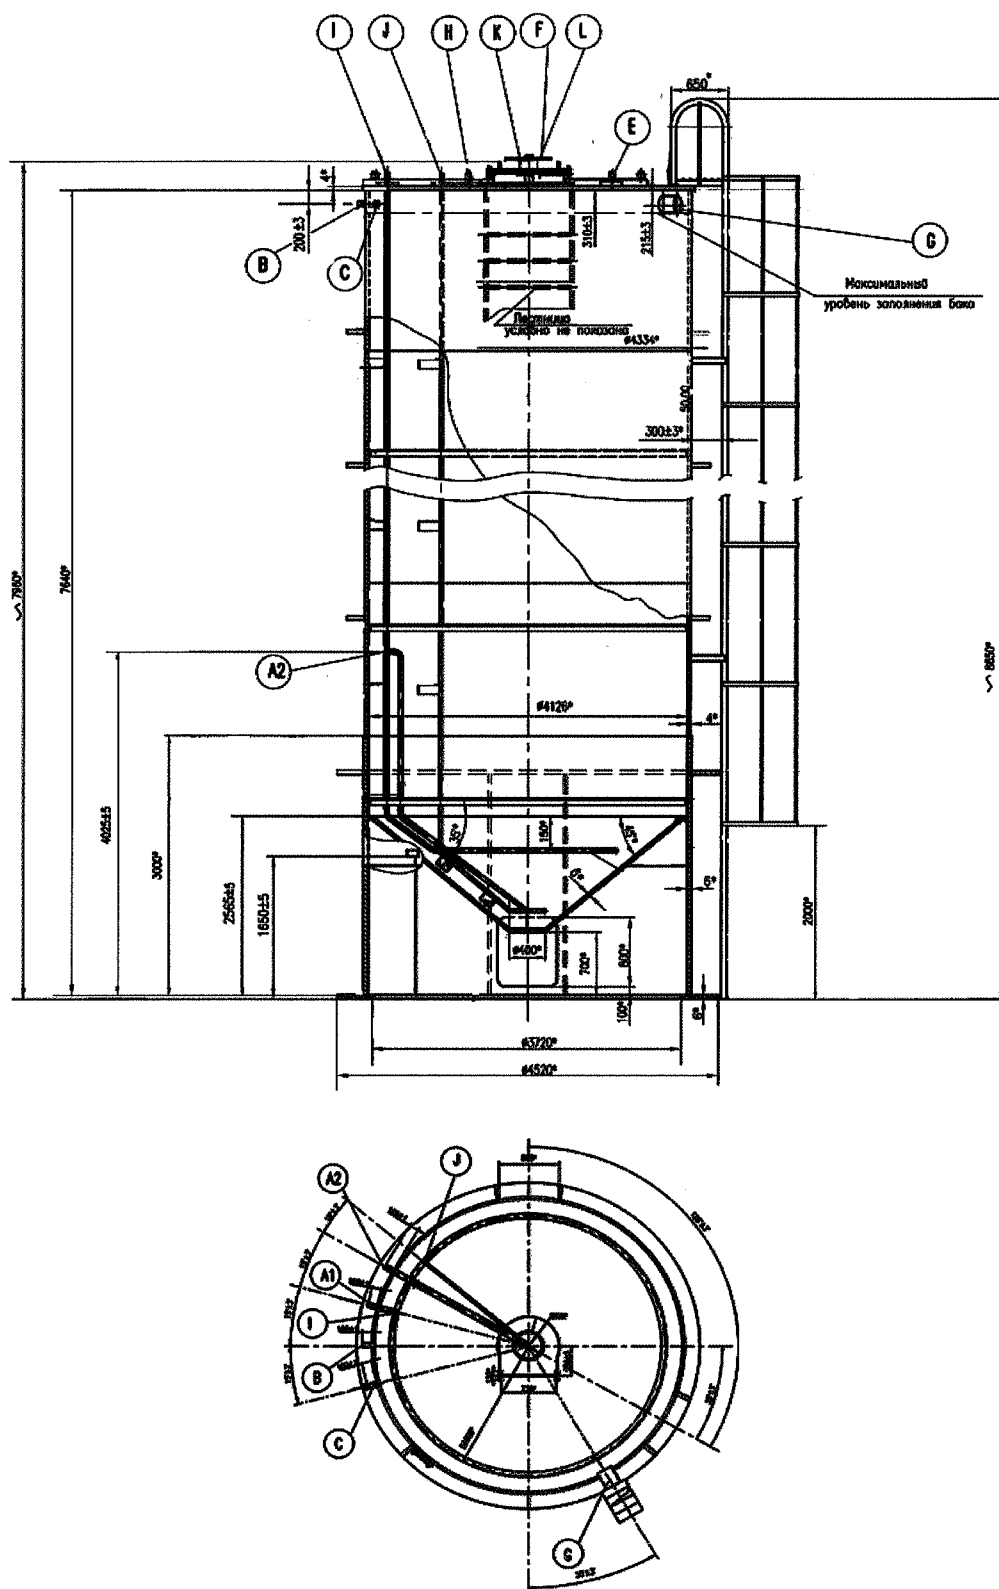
Габаритный чертеж баков кубового остатка с гидрозатвором с внутрикорпусным устройством КРК10ВВ001, КРК10ВВ002 и резервного бака КРК10ВВ003
